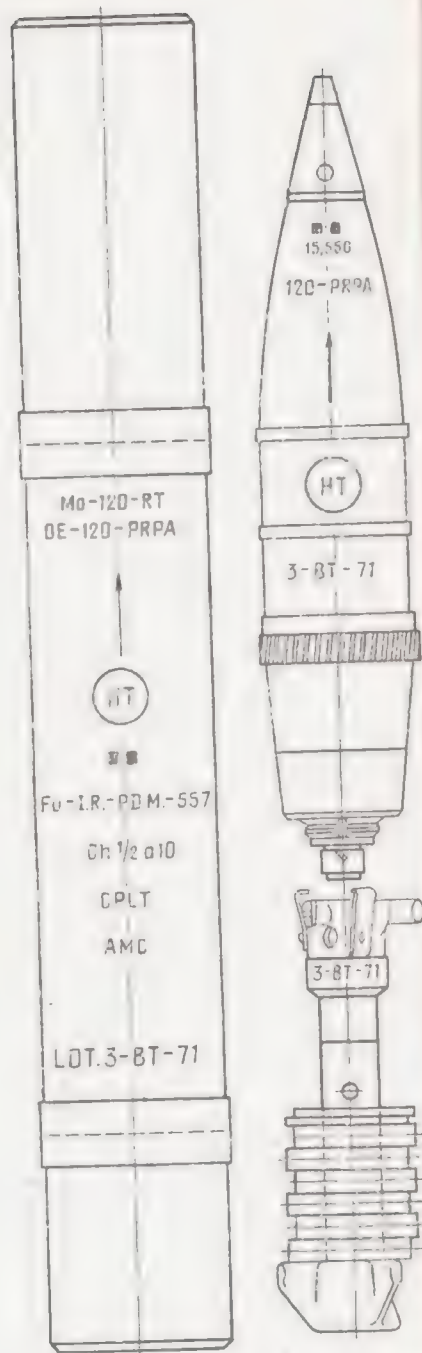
Образец маркировки активно-реактивного ОФ снаряда PRPA и укупорки для выстрела
